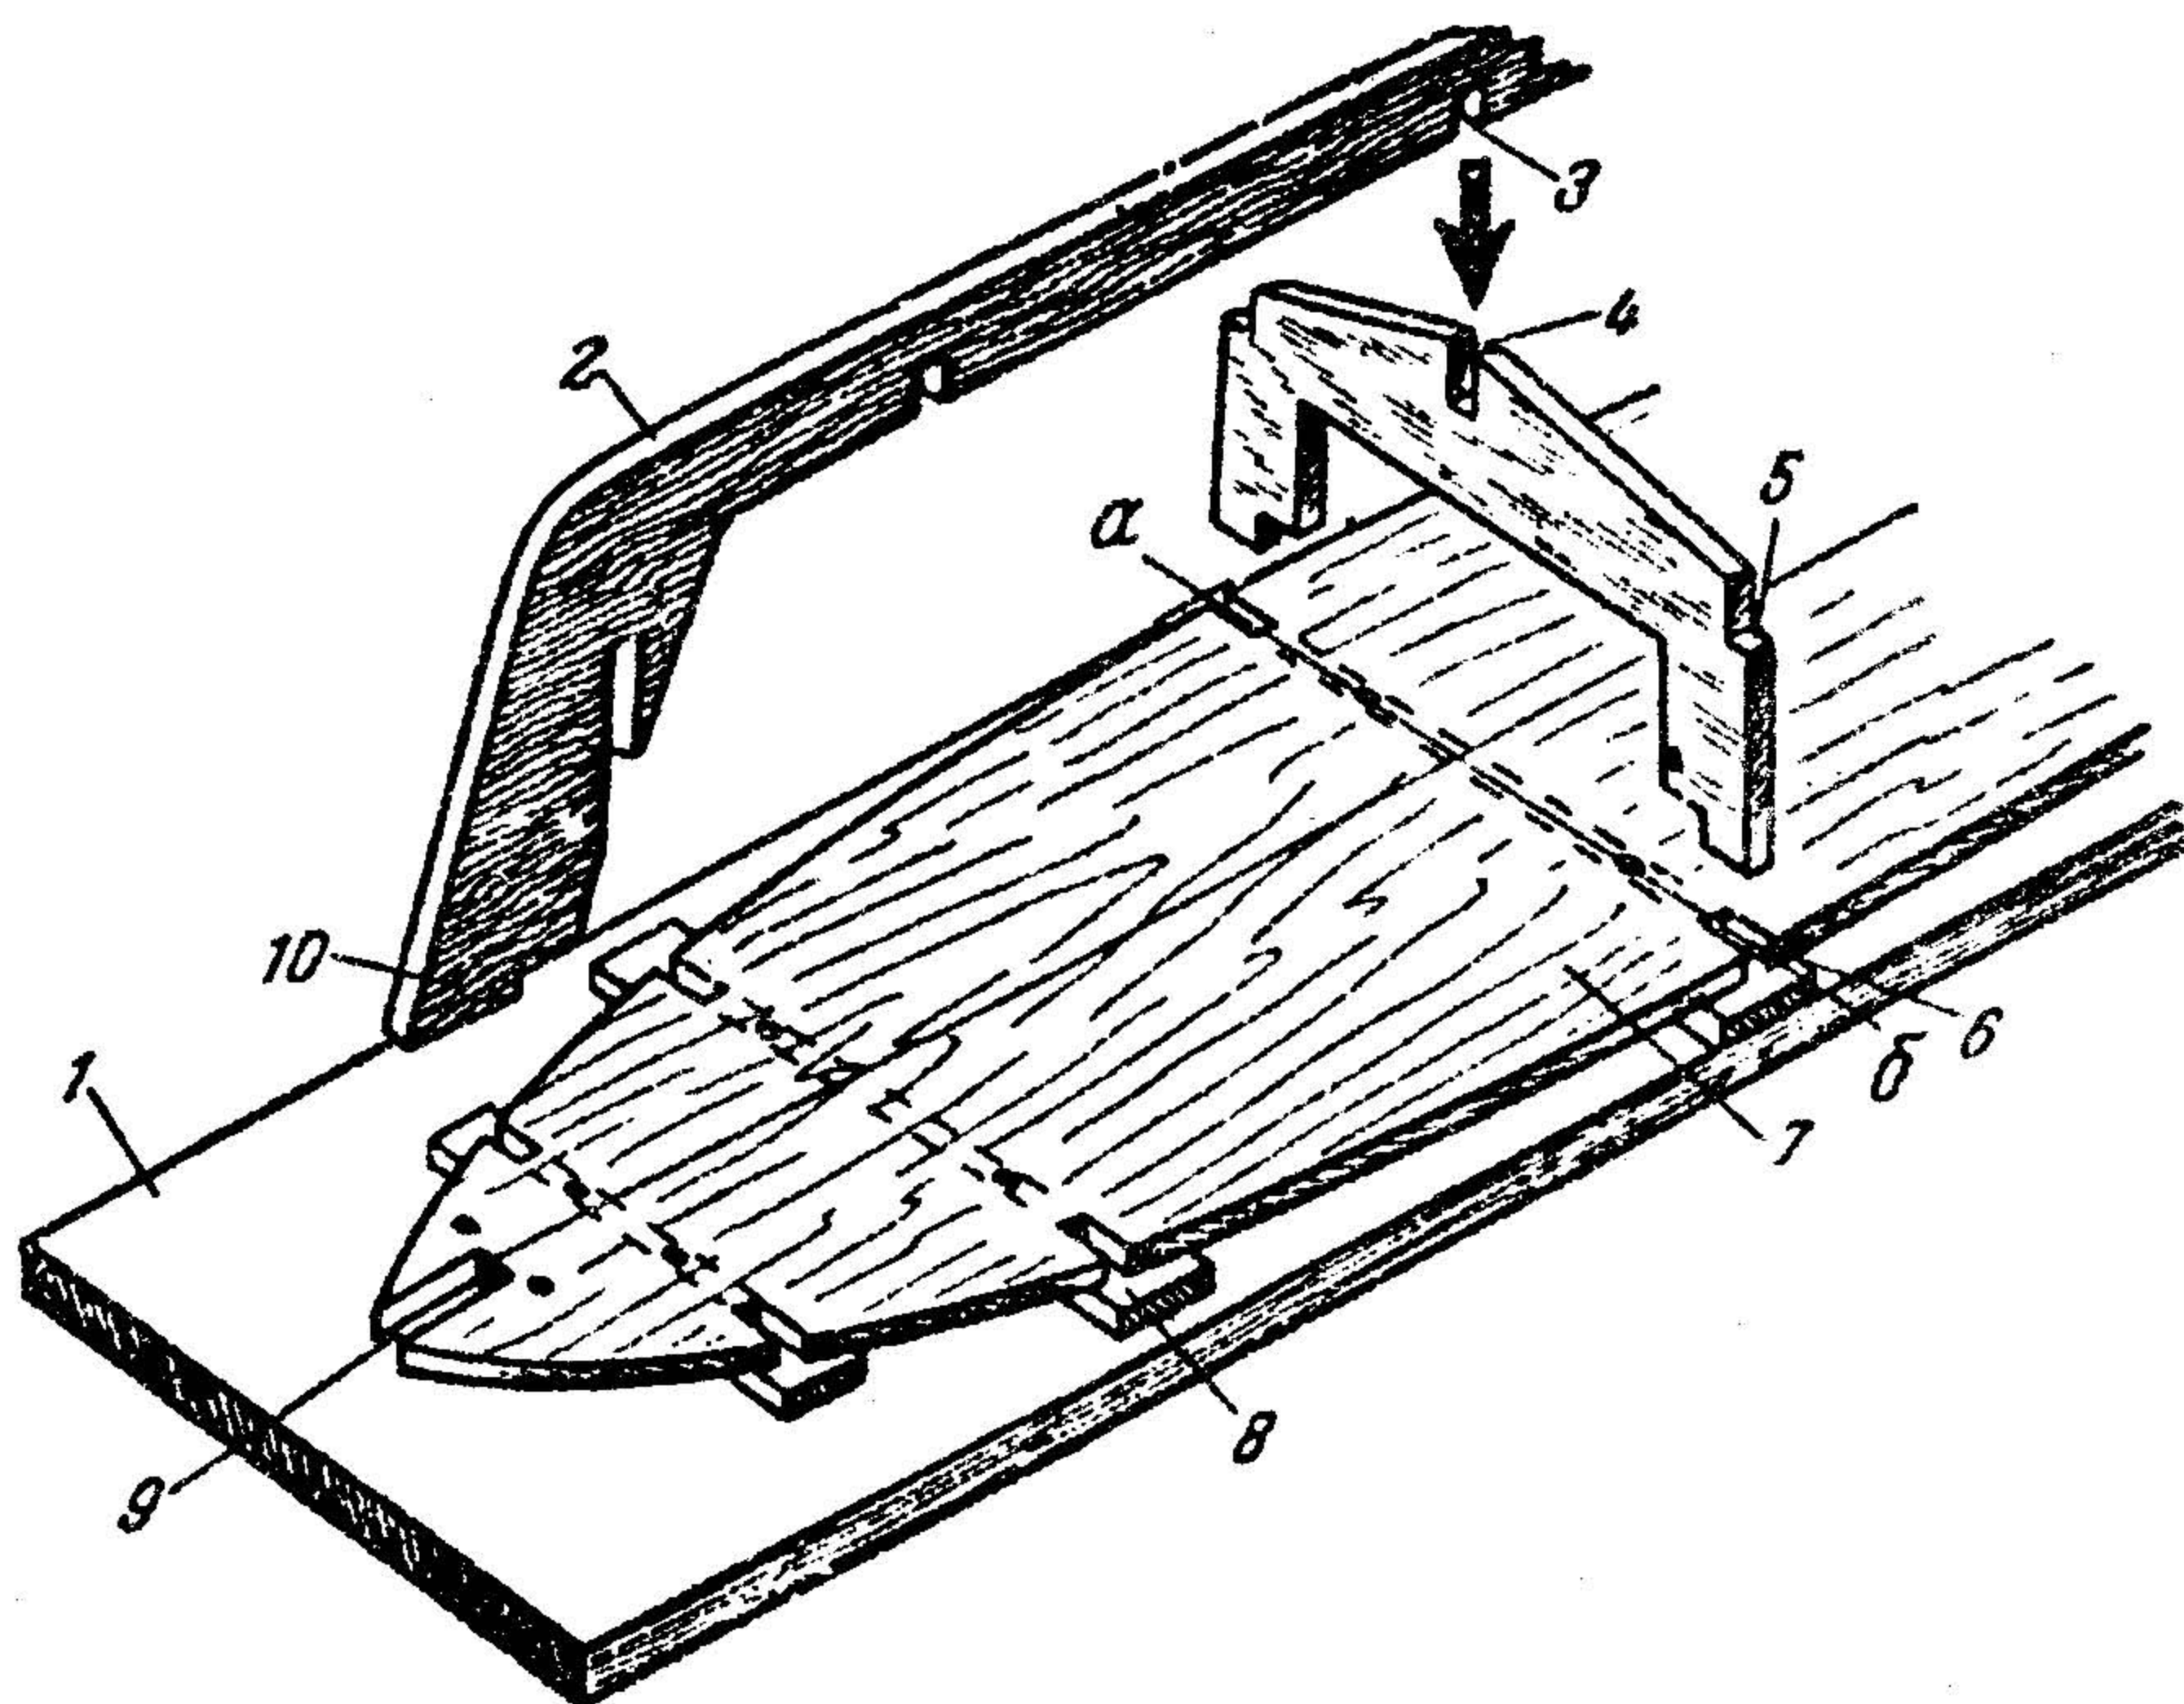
Установка килевой рамки: 1 — стапельная доска; 2—килевая рамка; 3 — вырез для шпангоута; 4 — вырез для килевой рамки; 5 — вырез для стрингера; 6 — вырез для шипа шпангоута; 7 — палубный настил; 8 — стапельный брусок; 9 — вырез для ахтерштевня; 10 — шип ахтерштевня
